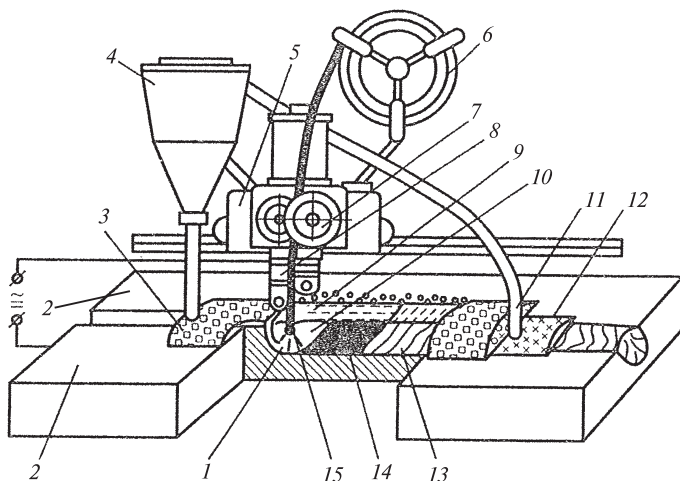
Схема автоматической сварки под флюсом:
